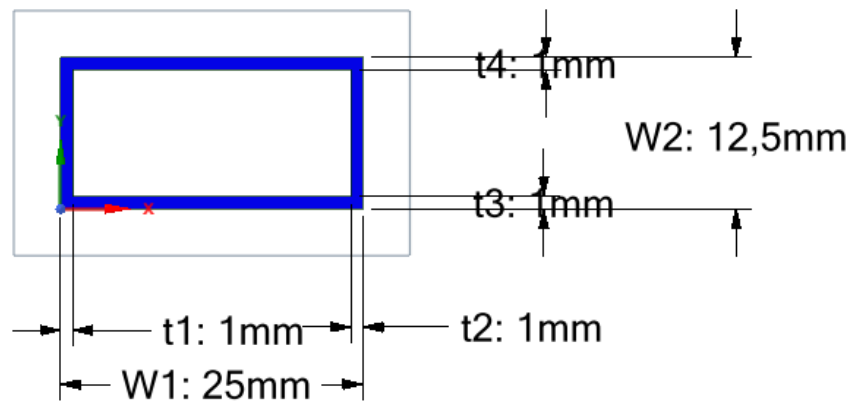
Perfil da viga, sem escala (Autores, 2021)
